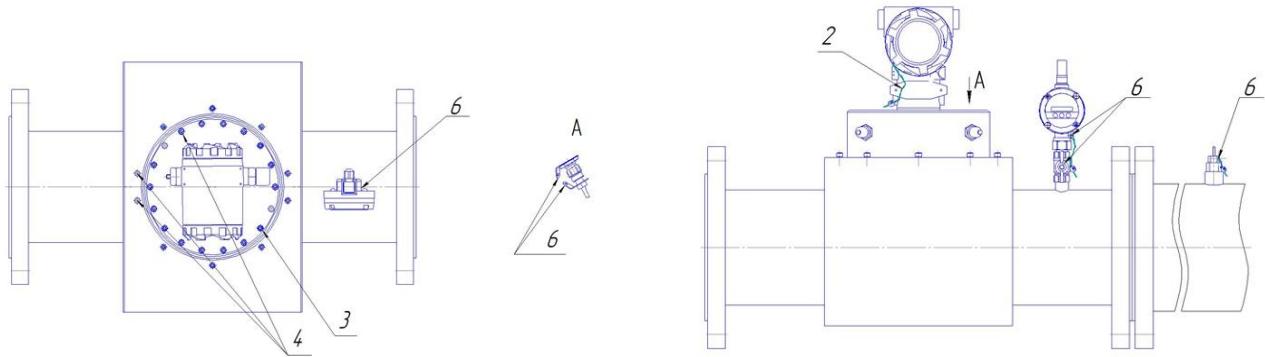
Корпус круглого сечения с защитным кожухом
